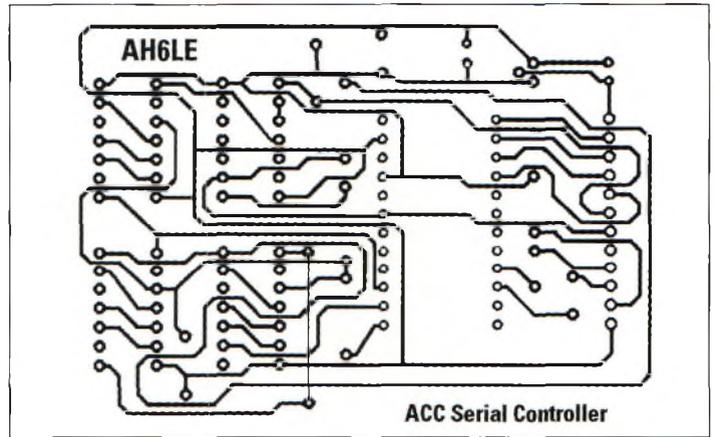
Carte de circuit imprimé du convertisseur en série, côté soudure.
